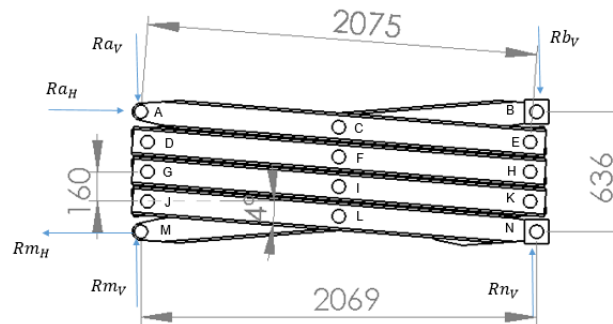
Fuerzas sobre la estructura extensible. Posición inferior
